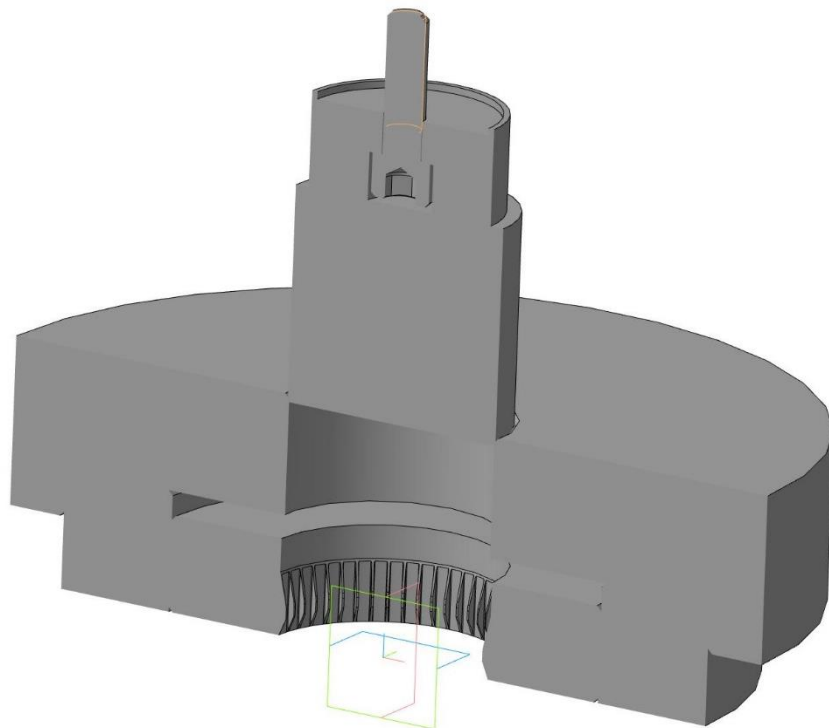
3D модель штампа для холодного видавлювання алюмінієвої деталі сердечник.
